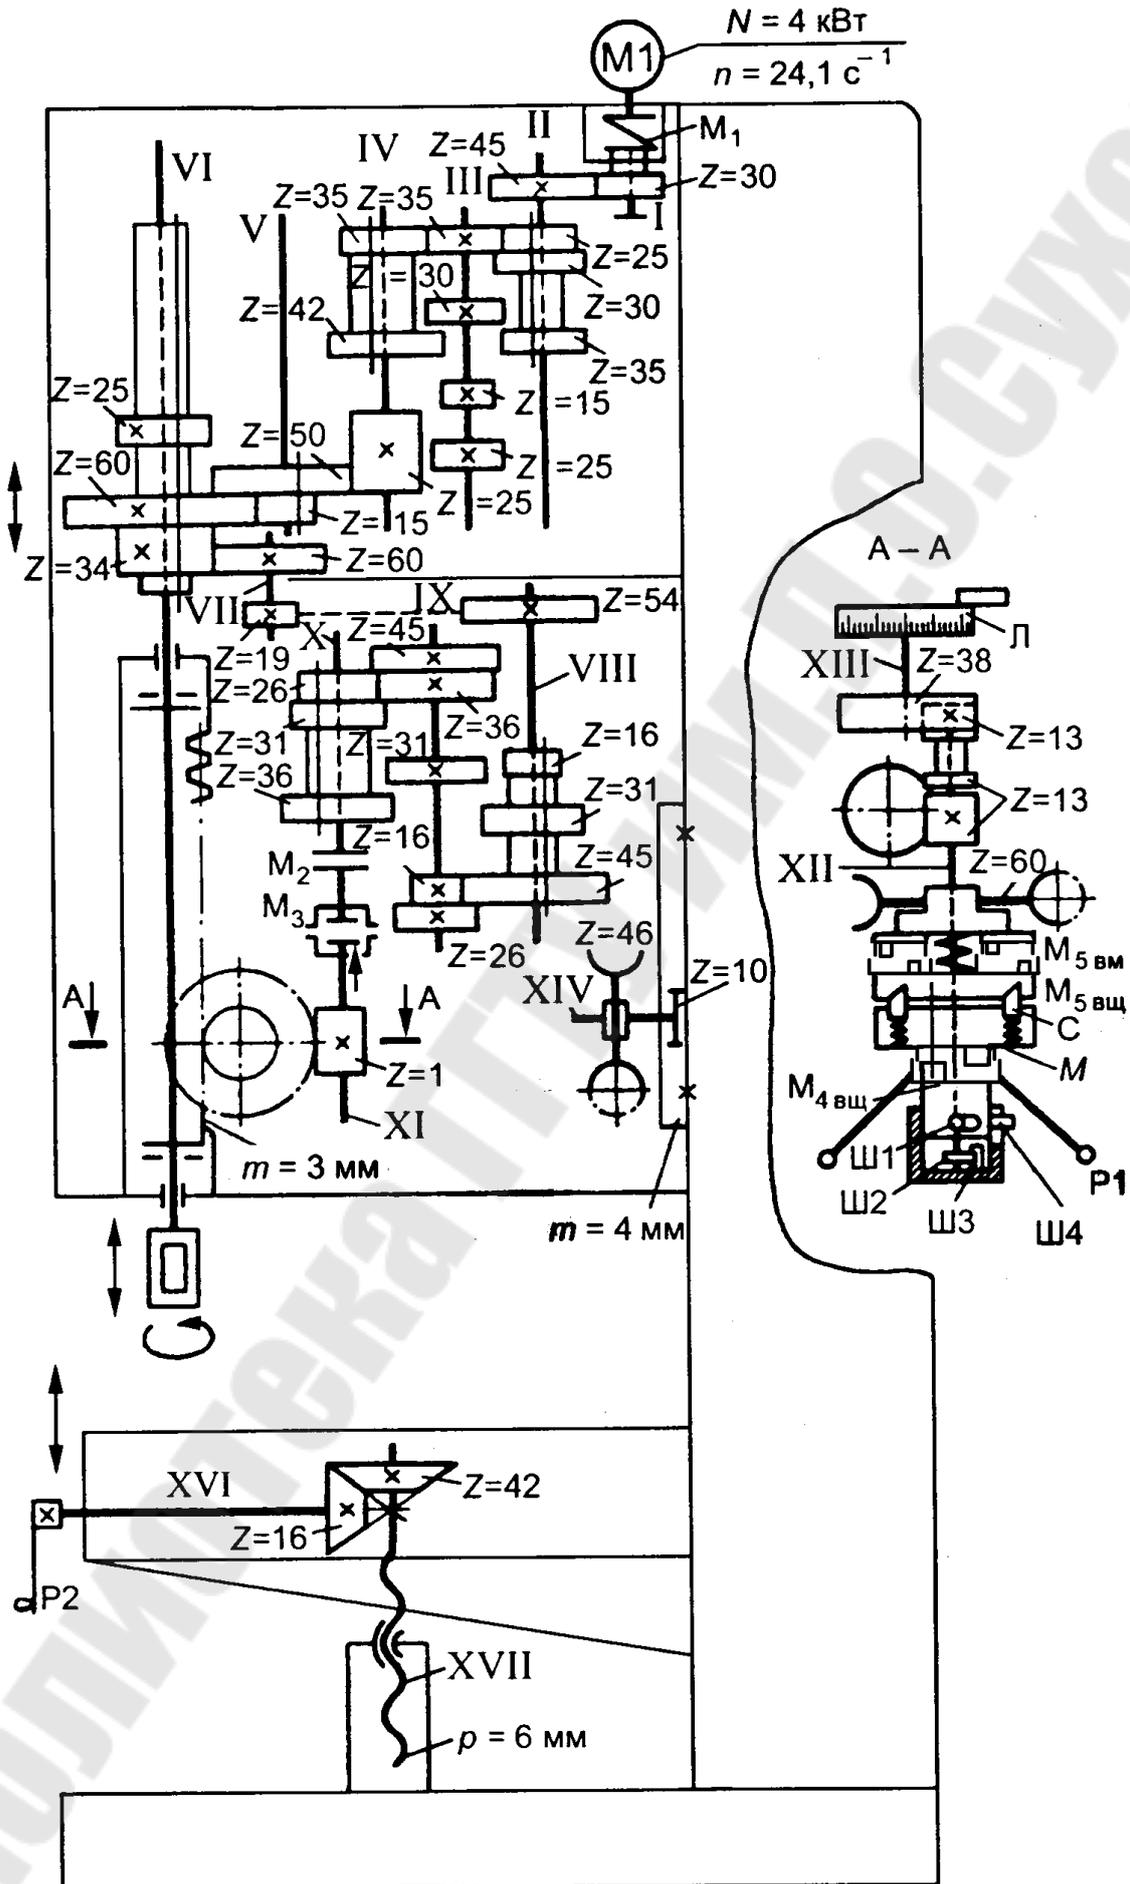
Кинематическая схема вертикально-сверлильного станка
